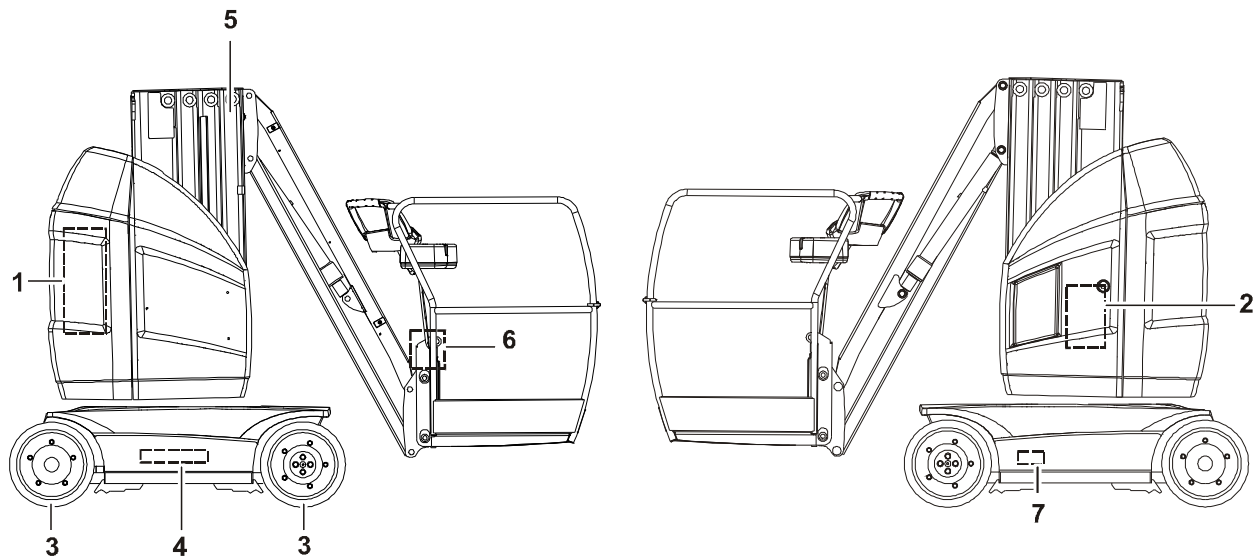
Схема техобслуживания и смазки силами оператора - 8E/20E
